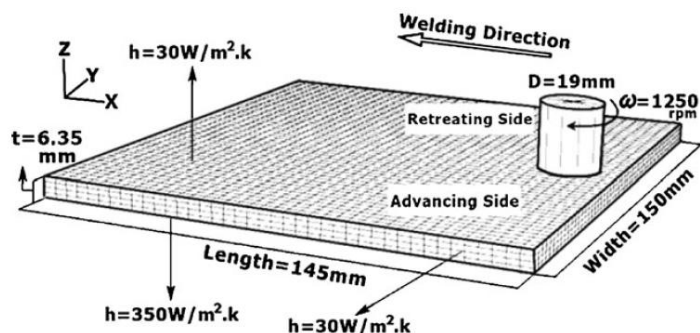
Зразок зварного з'єднання ЗТП з алюмінієвого сплаву 6061-T6 [13].
